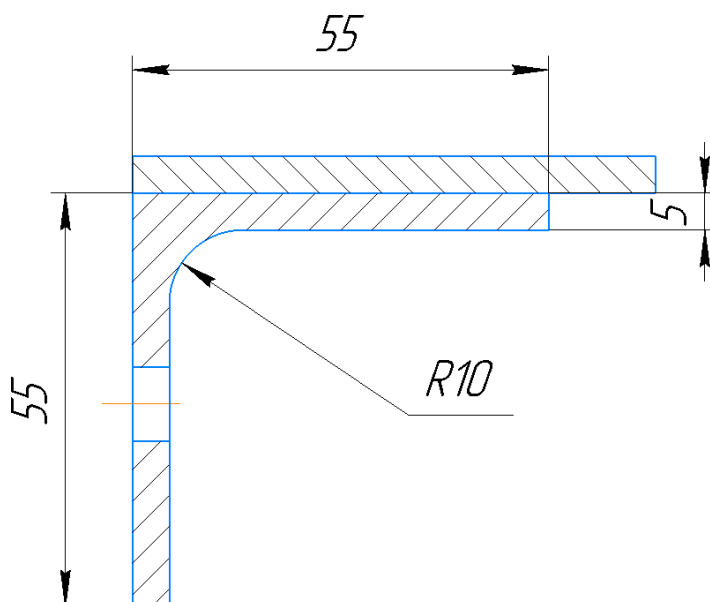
Опорный шпангоут, соединённый с обечайкой сварным соединением
